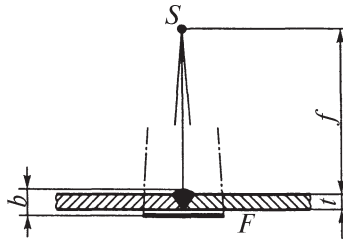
Схема получения снимка для плоского сварного шва и при просвечивании через одну стенку:
